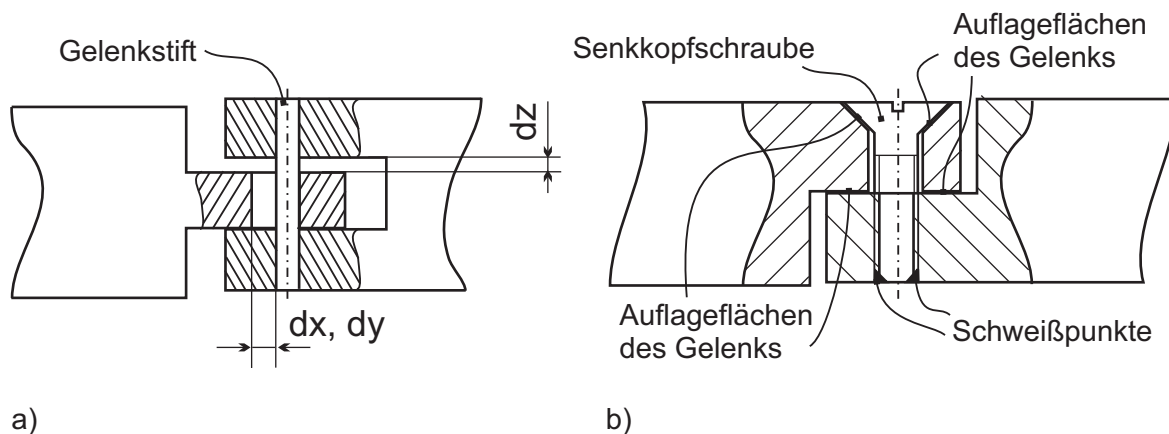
Verminderung des mechanischen Spiels innerhalb von Rotationsgelenken. a) Gelenk mit Gelenkstift und Gelenkspiel dx , dy , dz . b) montagefreundliches, spielarmes Gelenk, dessen Spiel beim Zusammenbau durch die Senkkopfschraube vermindert wird. Das Gelenk läuft an den Senkkopfflächen und an den aufeinanderliegenden Flächen der Gelenkpartner. Eine dauerhafte Verbindung mit Schweißpunkten (z.B. LASER-Schweißen) legt das Gelenkspiel fest.
